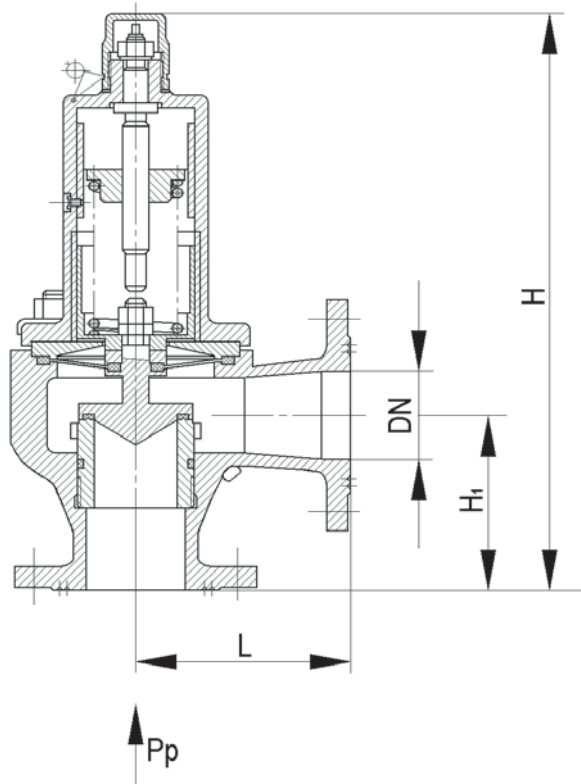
Клапан предохранительный угловой фланцевый
